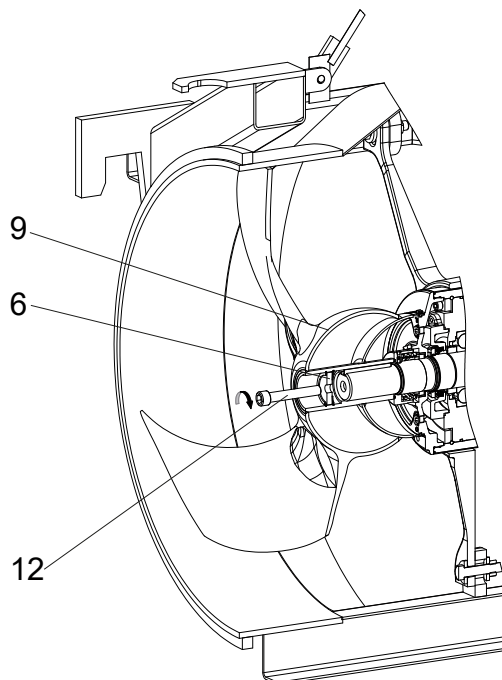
Rotor montage / demontage XRCP 800 PA
